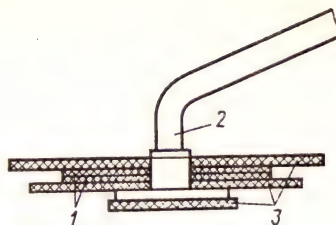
Сборка пятки вентиля камеры шины грузового автомобиля:
